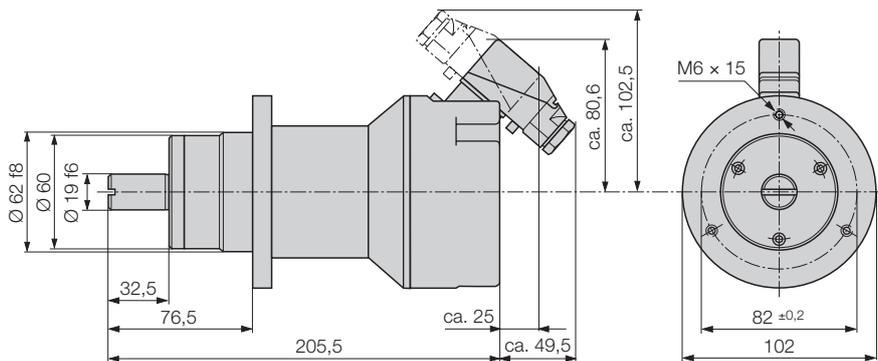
KINAX WT 707 mit Zusatzgetriebe und Steckverbinder.
